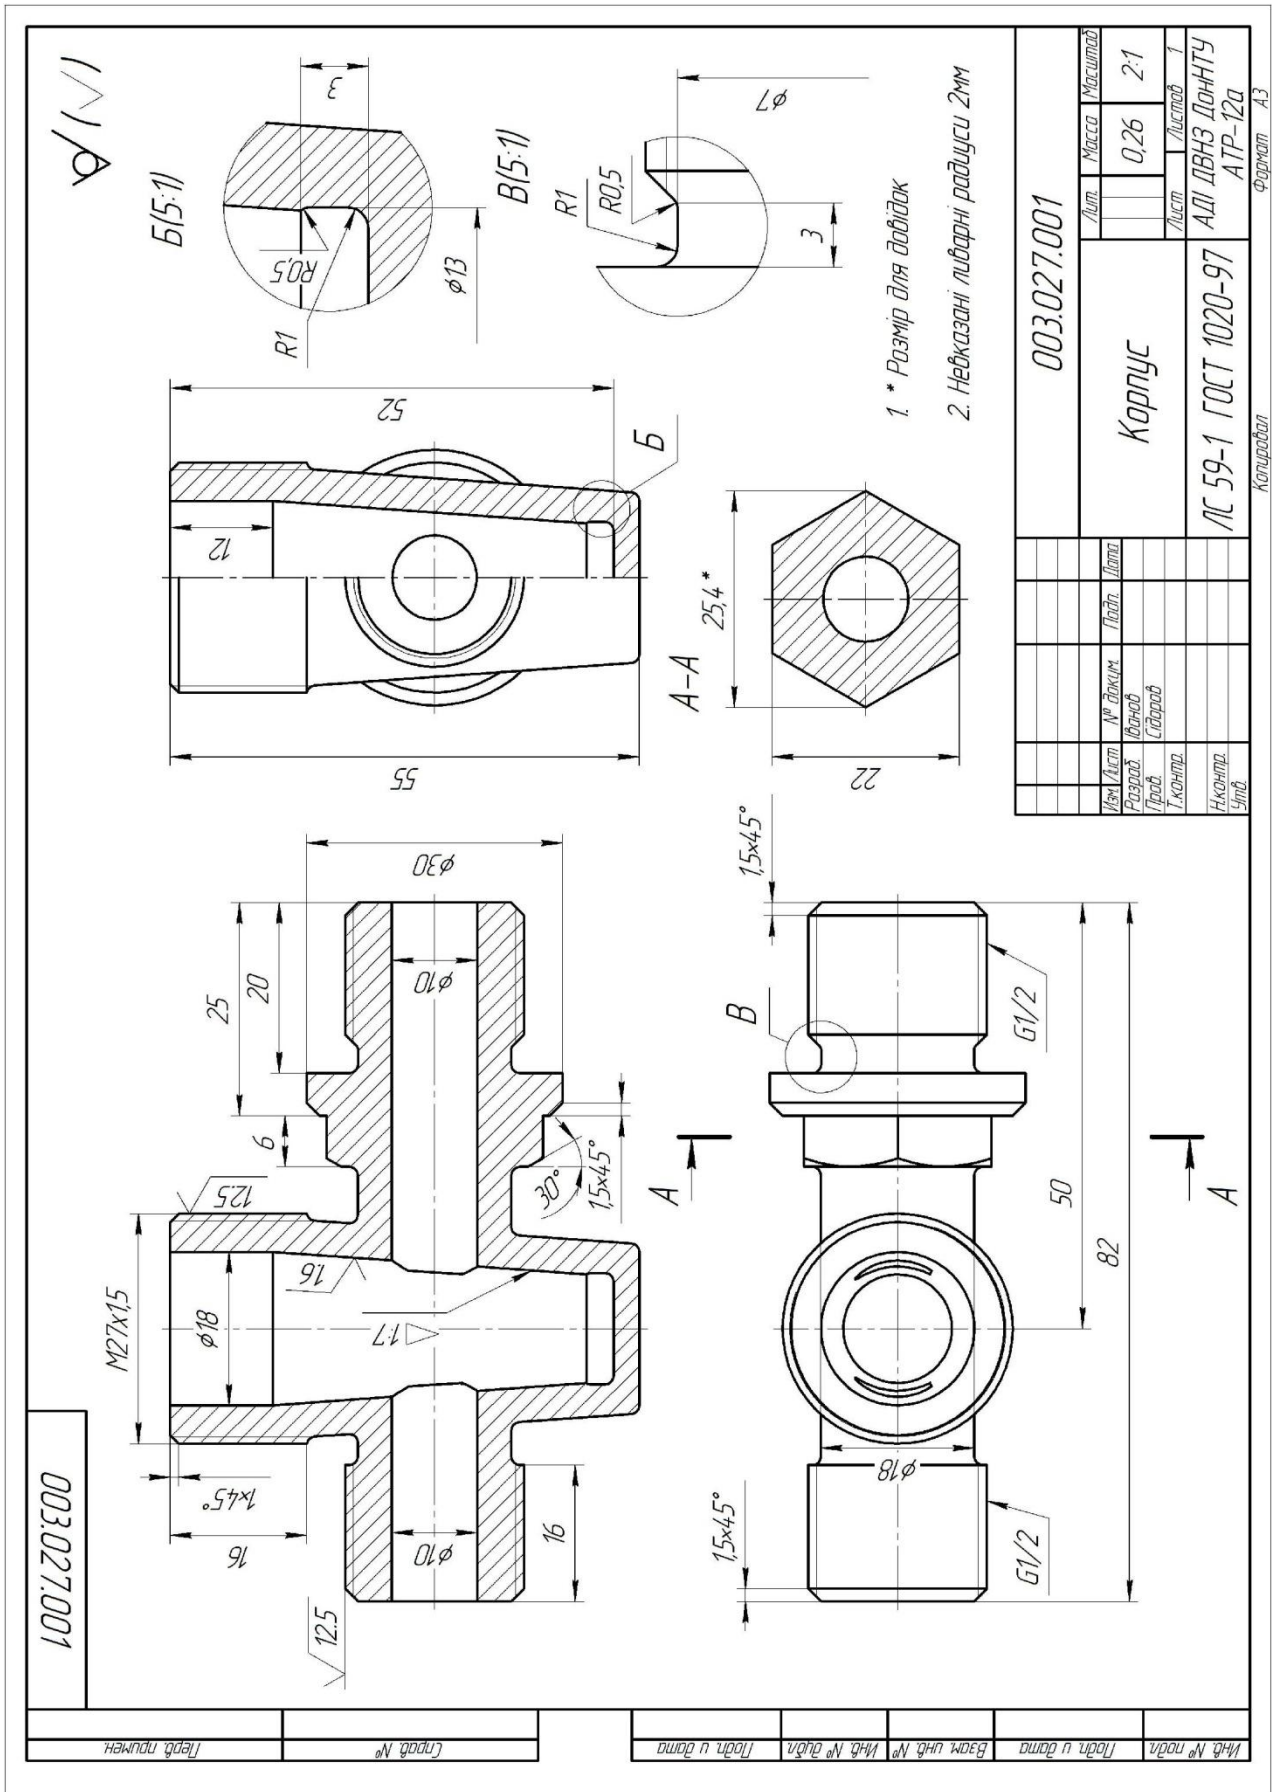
Приклад робочого креслення деталі «Корпус»
